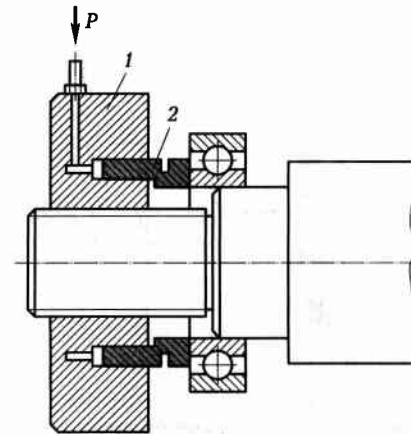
Гидравлическая гайка для запрессовки подшипников:
